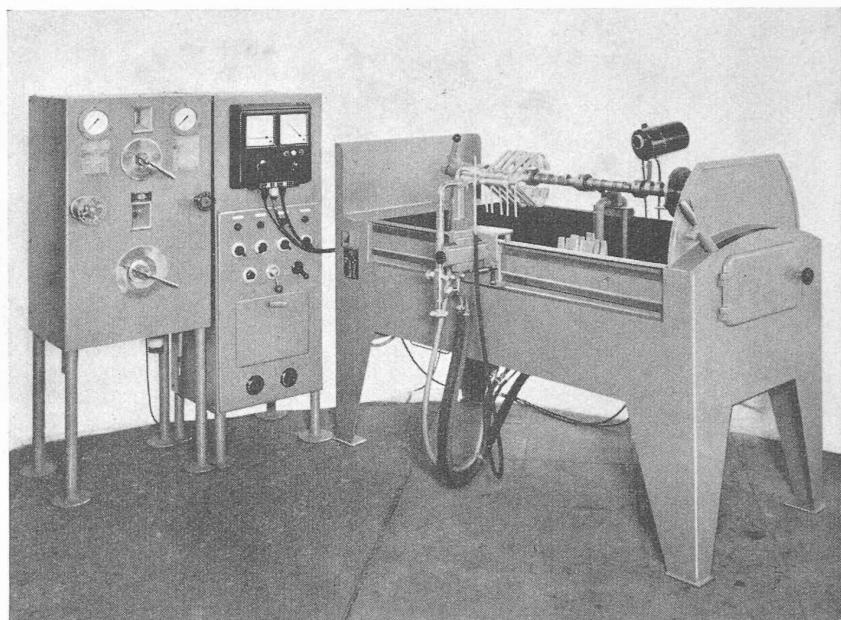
Machine à tremper les arbres à cames, avec milliscope et dispositif compteur.
